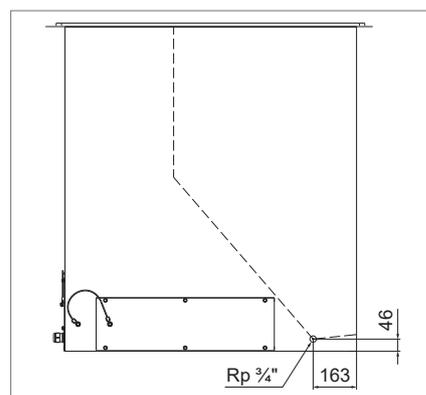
Dimensions du raccordement de la conduite d'évacuation des condensats/huiles (en mm)
